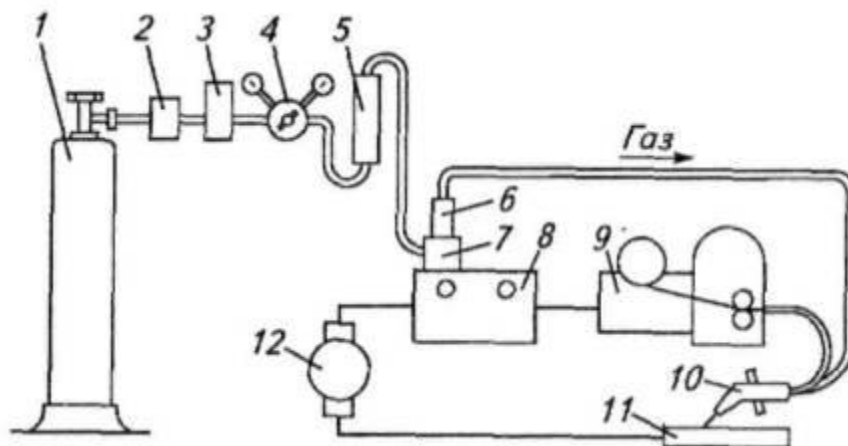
Схема установки для сварки (наплавки) в среде диоксида углерода: 1 - баллон с диоксидом углерода; 2 - электрический подогреватель газа; 3 - осушитель газа; 4 - газовый редуктор; 5 - ротаметр (расходомер газа); 6, 7 - электромагнитный газовый клапан; 8 - аппаратный ящик; 9 - механизм подачи проволоки с катушкой; 10 - сварочная горелка; 11 - восстанавливаемая деталь; 12 - источник сварочного тока
